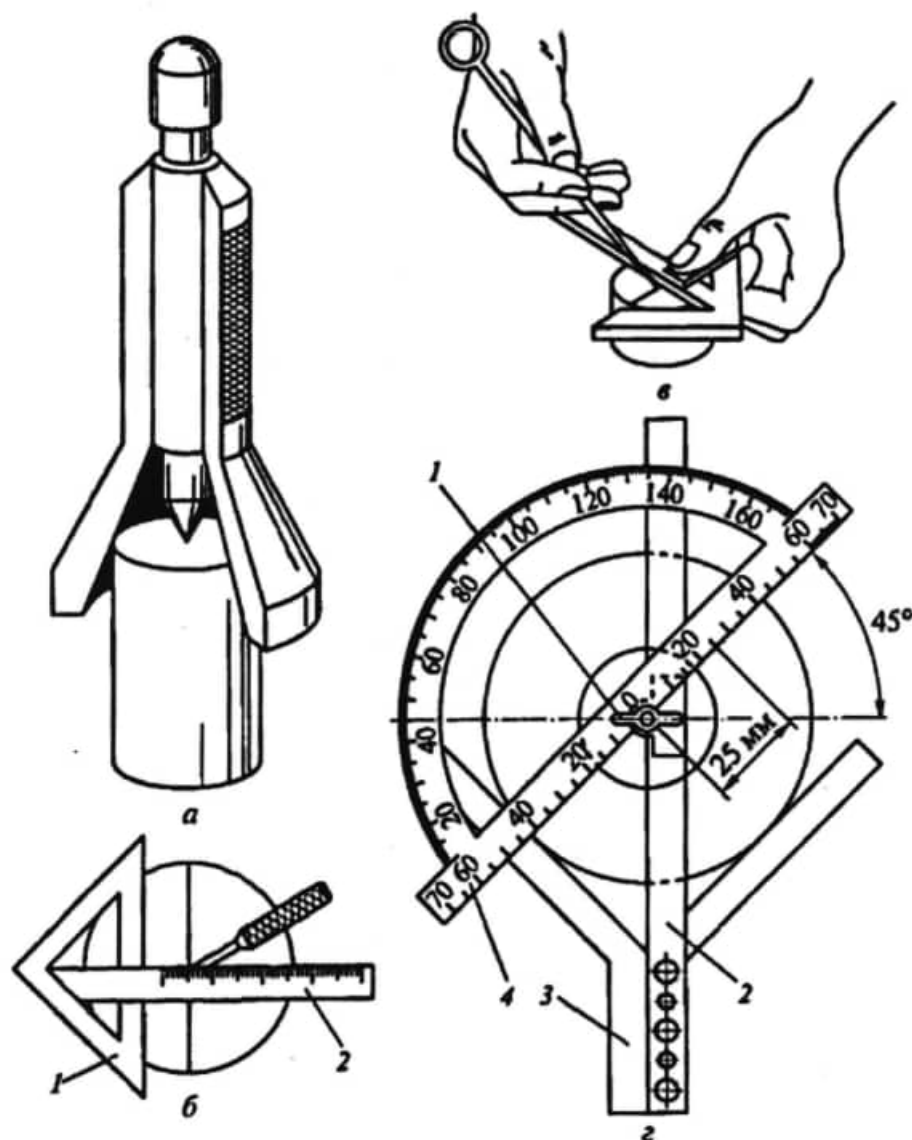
Инструменты для нанесения центровых отверстий:
